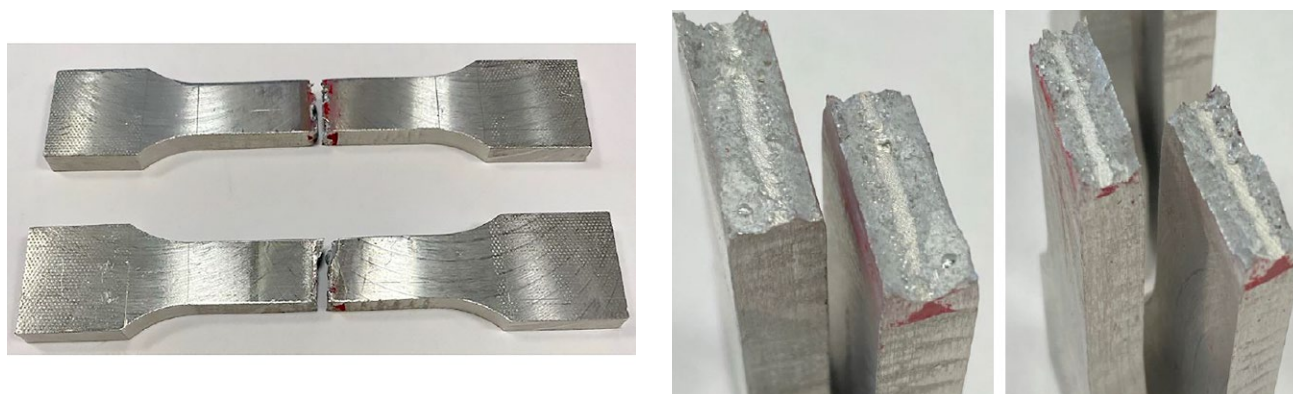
Разорванные образцы из напечатанного алюминия, сваренного с листовым АМг5.
